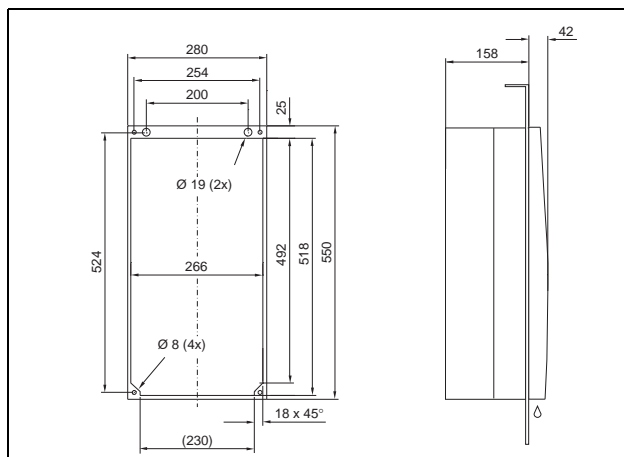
SK 3304.xxx, SK 3305.xxx, pro úplné zapuštění
